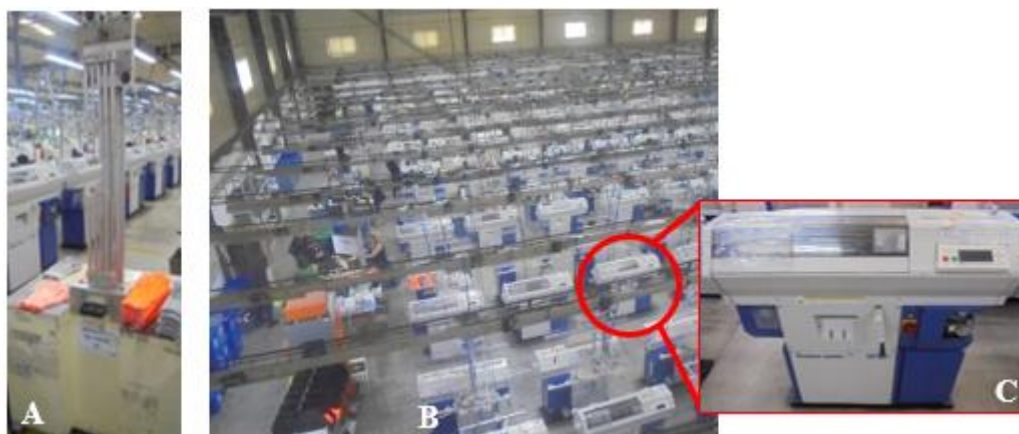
A: Máquina de virar; B: Zona de tricotagem (máquinas operam sozinhas); C: Máquina de tricotar automática
